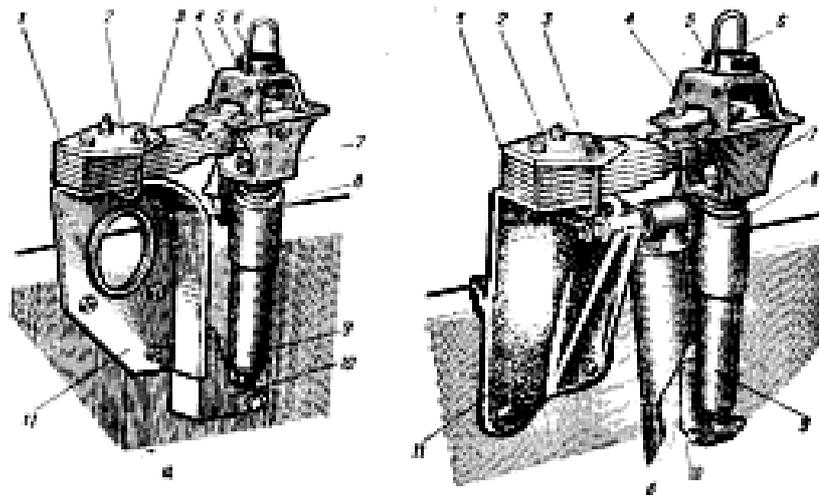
Задняя опора кабины: а - автомобиля Камаз-5320; б - автомобиля Камаз-4310;
